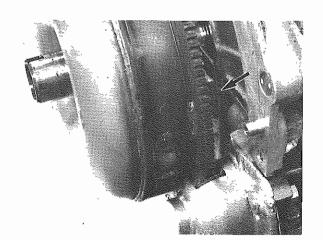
Viti di fissaggio convertitore Converter fixing bolts
